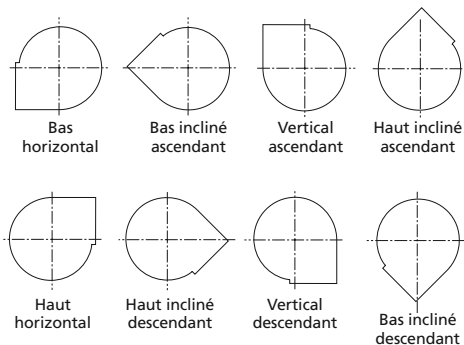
Refoulement de la soufflante, vue du côté moteur (sens des aiguilles d'une montre)
